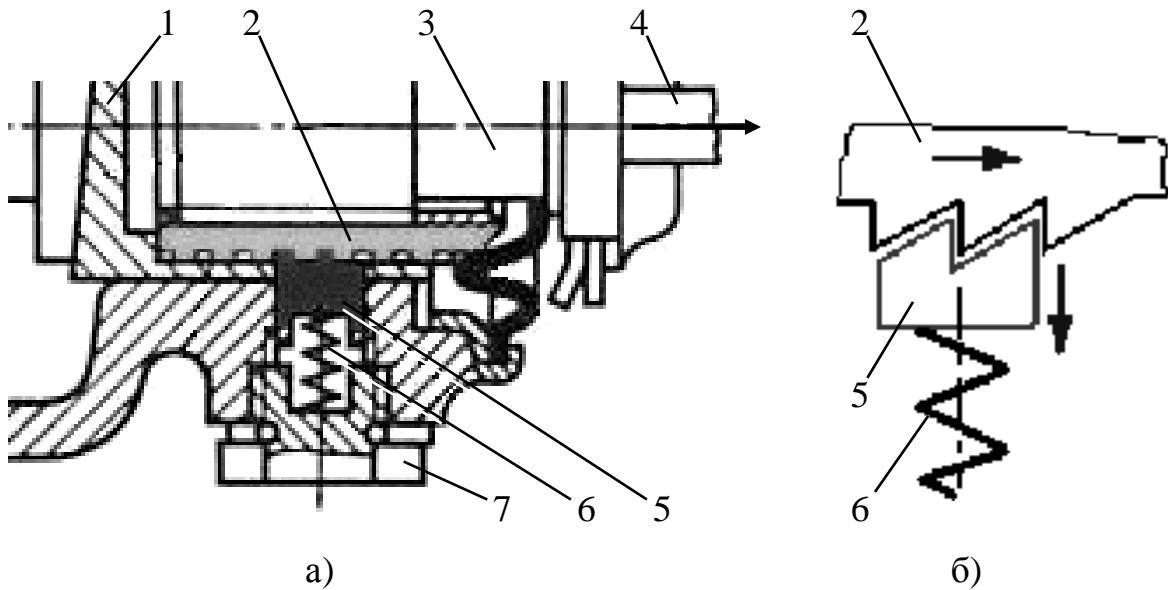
Устройство автоматической регулировки зазора между тормозными колодками и барабаном тормозного механизма с клиновым разжимным устройством: а – конструкция, б – схема храпового устройства; 1 – толкатель разжимного устройства; 2 – регулировочная втулка; 3 – регулировочный винт; 4 – ребро тормозной колодки; 5 – стопорный штифт; 6 – пружина; 7 – заглушка
